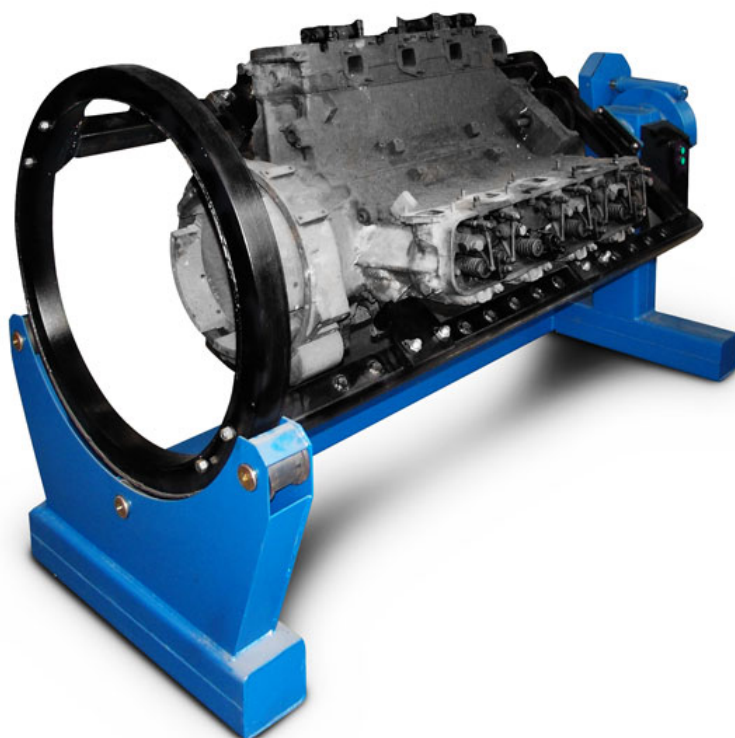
Стенд для разборки - сборки V-образных двигателей P770E
